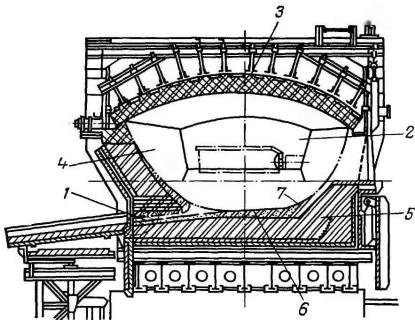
Поперечный разрез мартеновской печи с основной футеровкой: 1 — сталевыпускное отверстие; 2 — задняя стенка; 3 — главный свод; 4 — рабочее пространство; 5 — передняя стенка; 6 — подина; 7 — слой магнезитовой наварки
